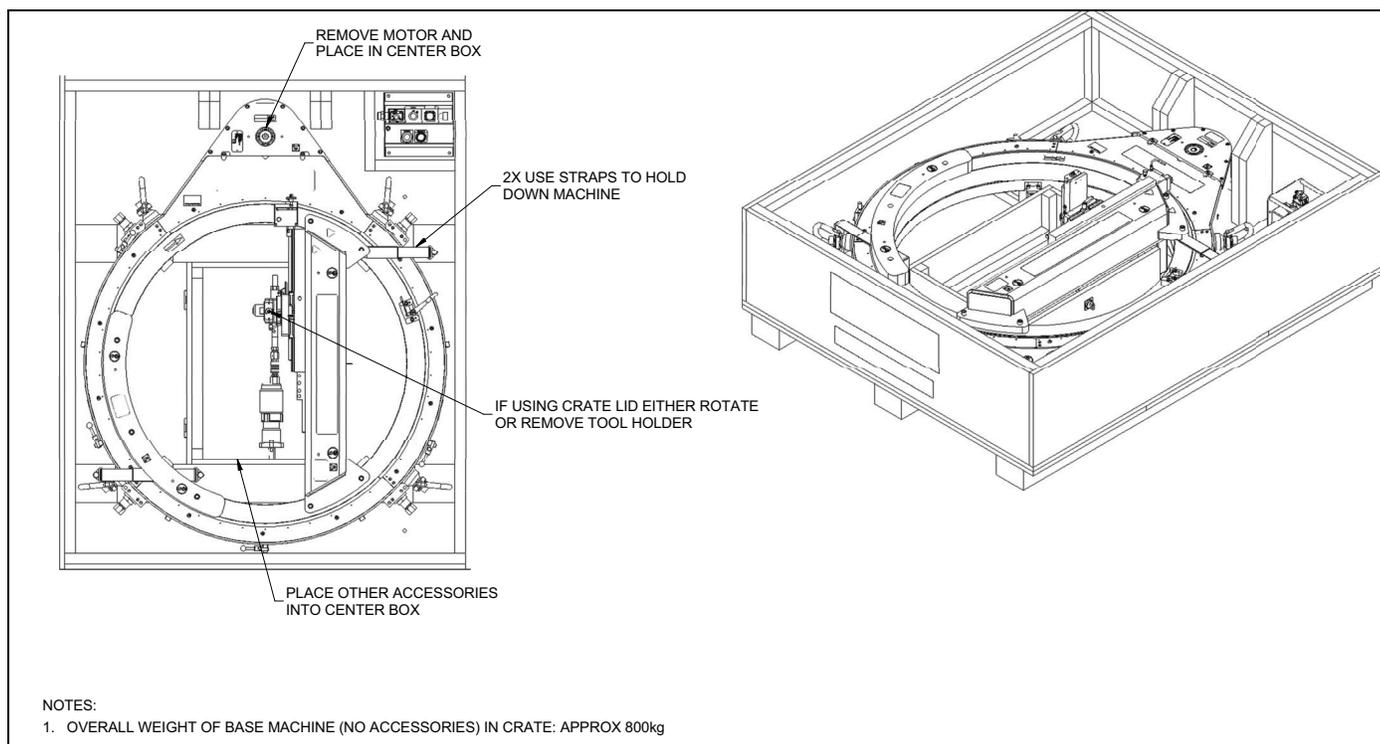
CAISSE D'EXPÉDITION DE LA MACHINE ODF40
